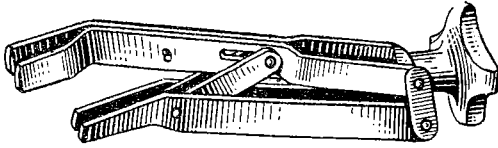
Приспособление для снятия клапанных пружин двигателя
